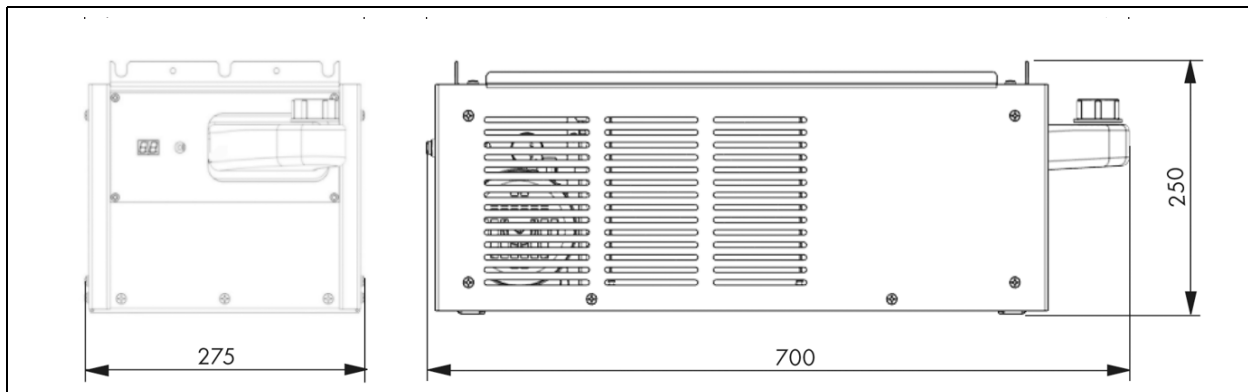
Abmessungen Umlaufkühlgerät iROB Cool
